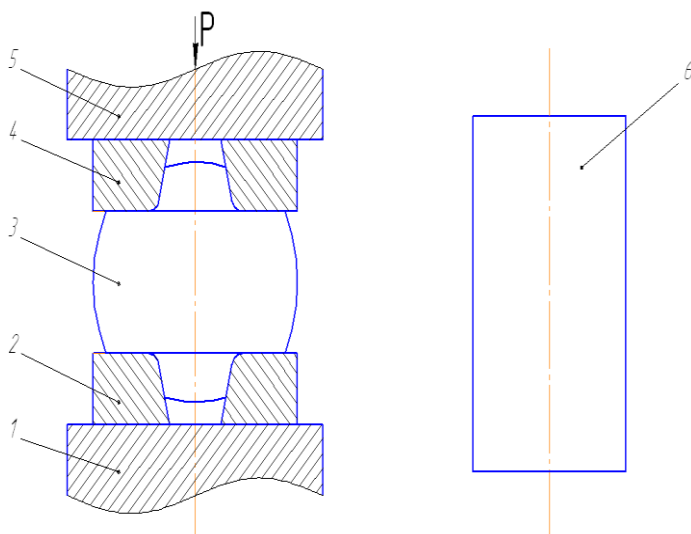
Схема осадки цилиндрических заготовок в подкладных кольцах:
